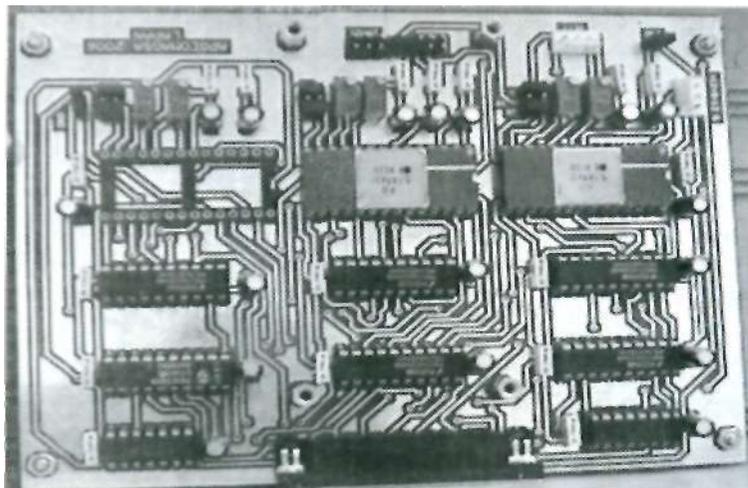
Lay out PCB tata letak komponen modul op-amp
